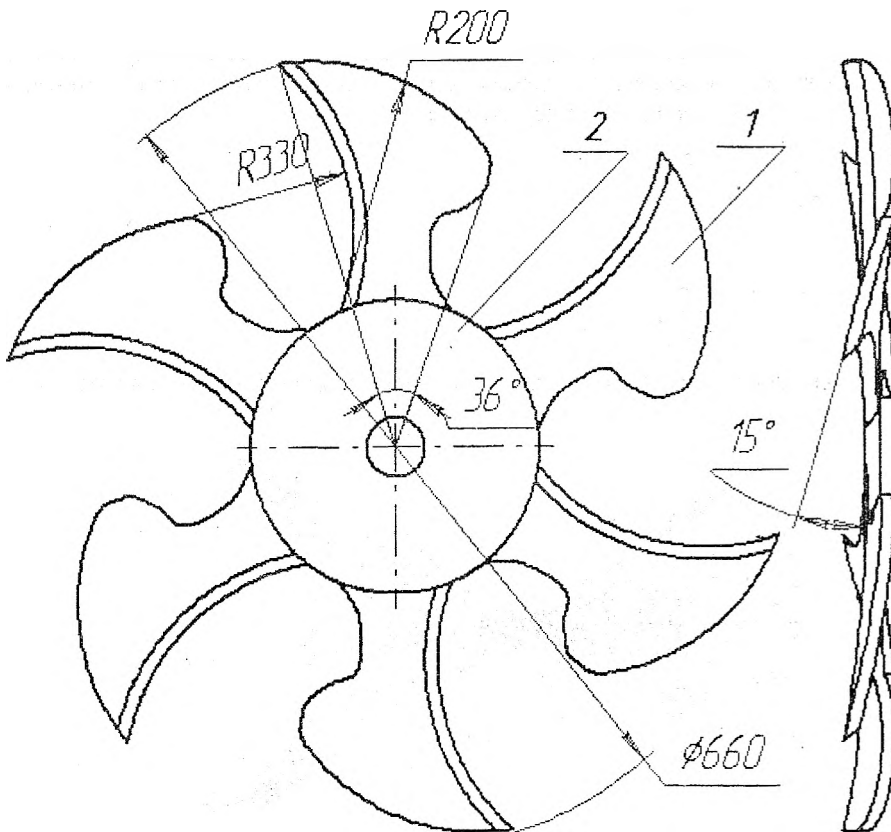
Ротатійний робочий орган з гіперболічними ножами-лопатями:
